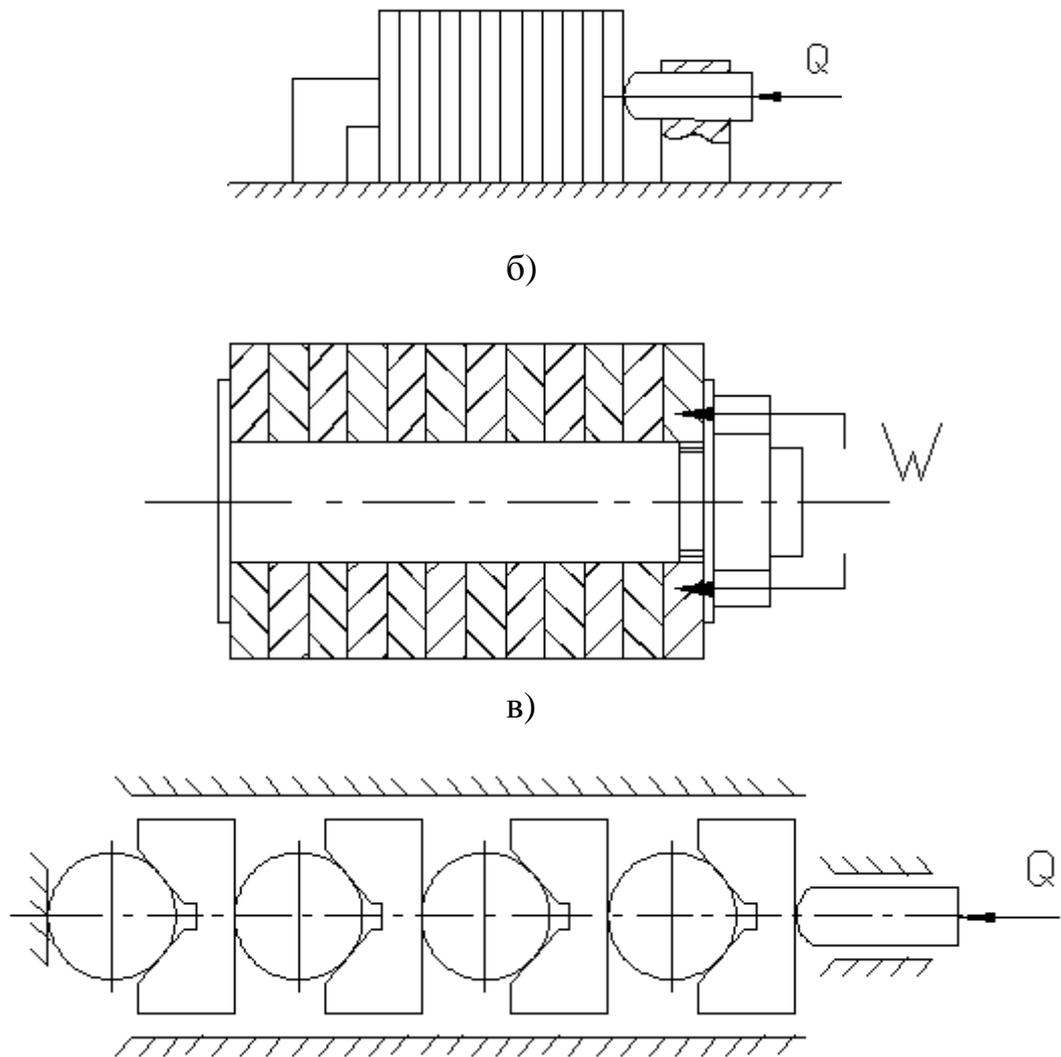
Схемы зажимных механизмов последовательного действия: а – зажим пакета заготовок в тисках; б – зажим пакета заготовок на оправке; в – зажим заготовок в призмах.
